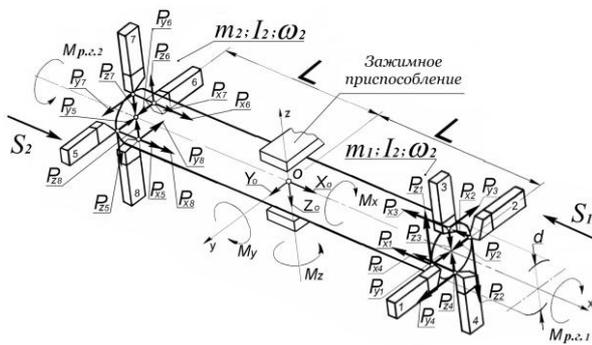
Схема нарезания резьбы на заготовке из ПКМ резцовыми головками. показателей.
